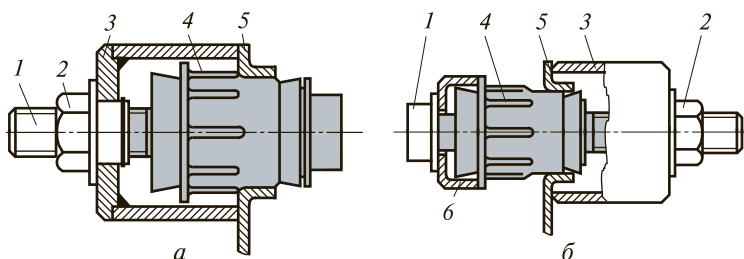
Схемы выпрессовки (а) и запрессовки (б) шарнира верхнего рычага:
